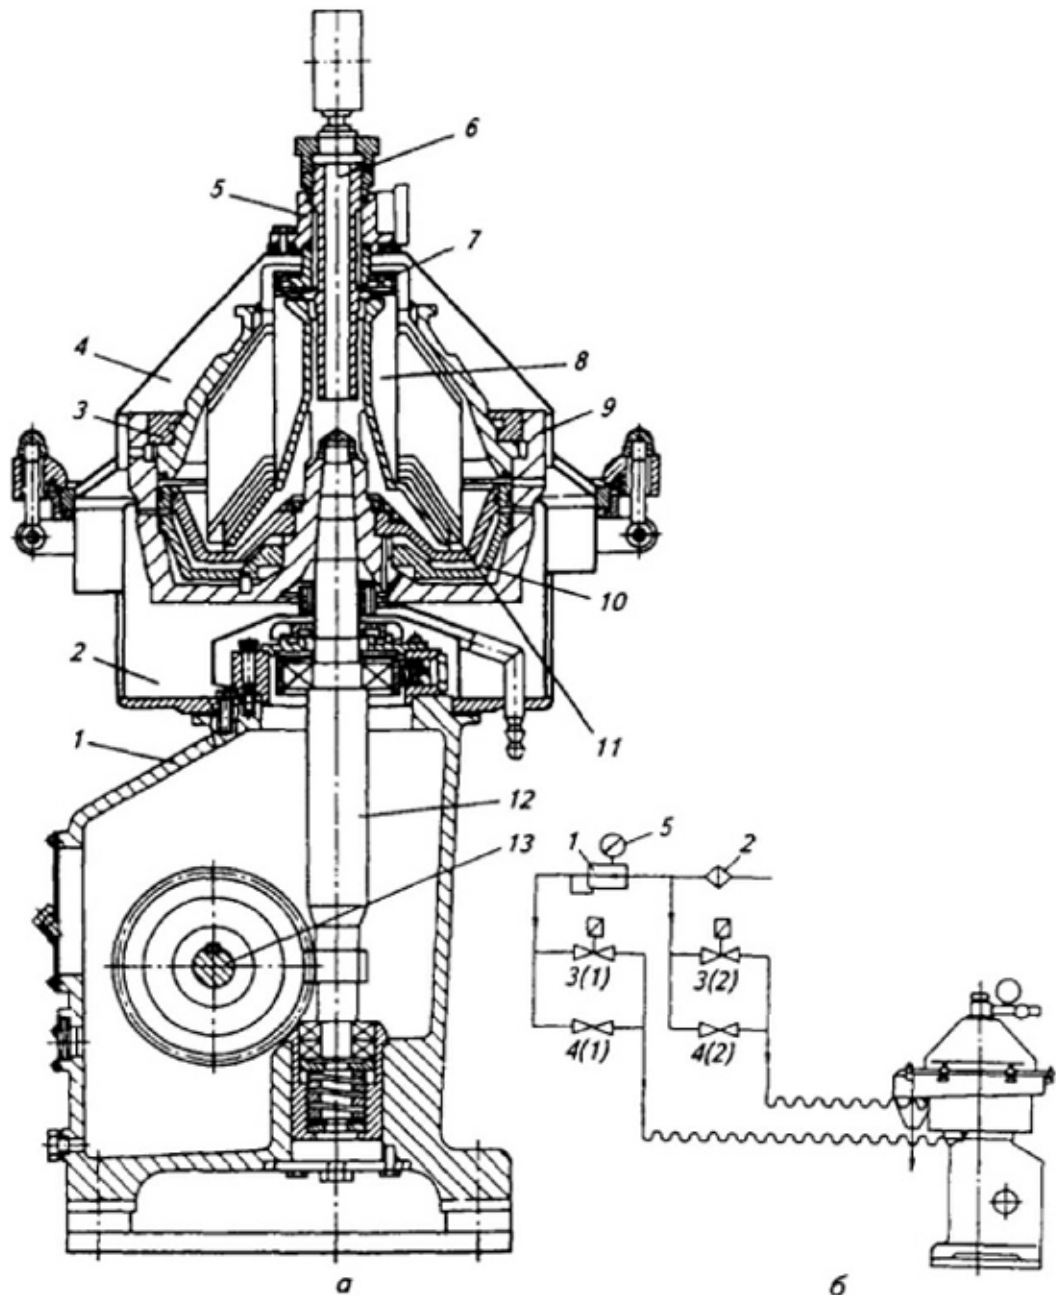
Сепаратор А1-ОЦМ-15: а – загальний вигляд: 1 – станина, 2 - приймач осаду, 3 – барабан, 4 – кришка сепаратора, 5 – приймально-розвантажувальний, 6 – центральна труба; 7- напірний диск; 8 – тарілотримач, 9 - основа, 10 – поршень, 11 - пакет тарілок, 12 – вертикальний вал, 13 - горизонтальний вал; б – схема підключення гідросистеми: 1 – редукційний клапан, 2 – фільтр, 3(1), 3(2) – електромагнітні клапани, 4 (1), 4 (2) – вентилі, 5 - манометр
